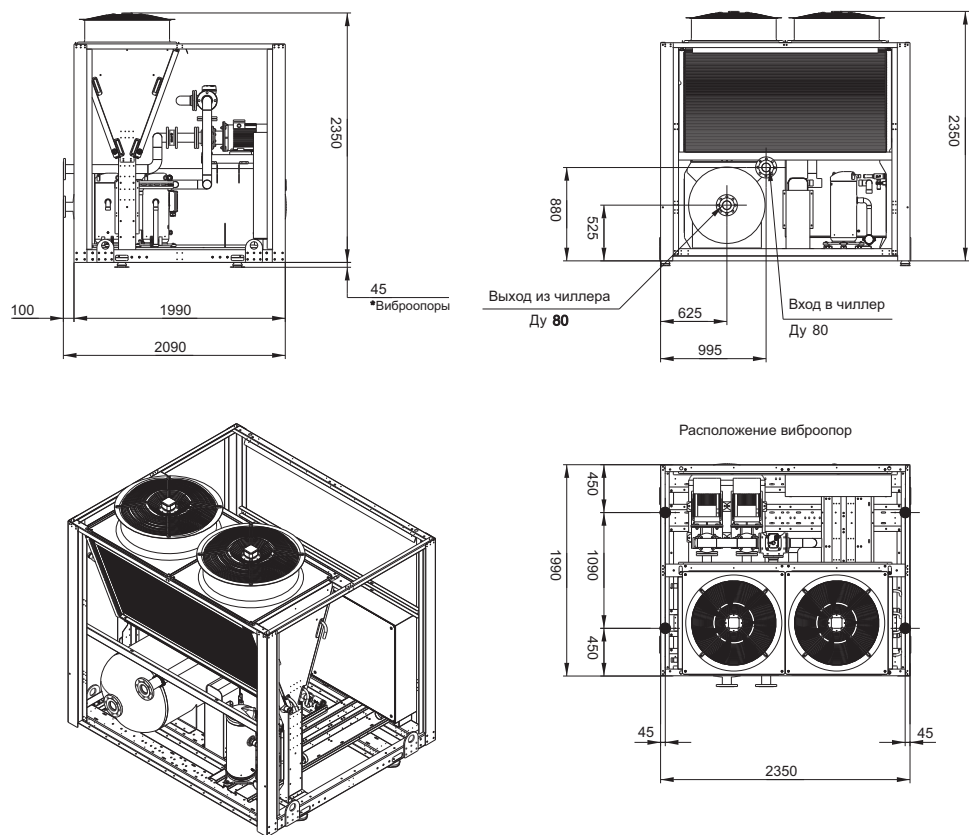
Внешний вид и габаритные размеры ЧМ CH-RHAE-0128
